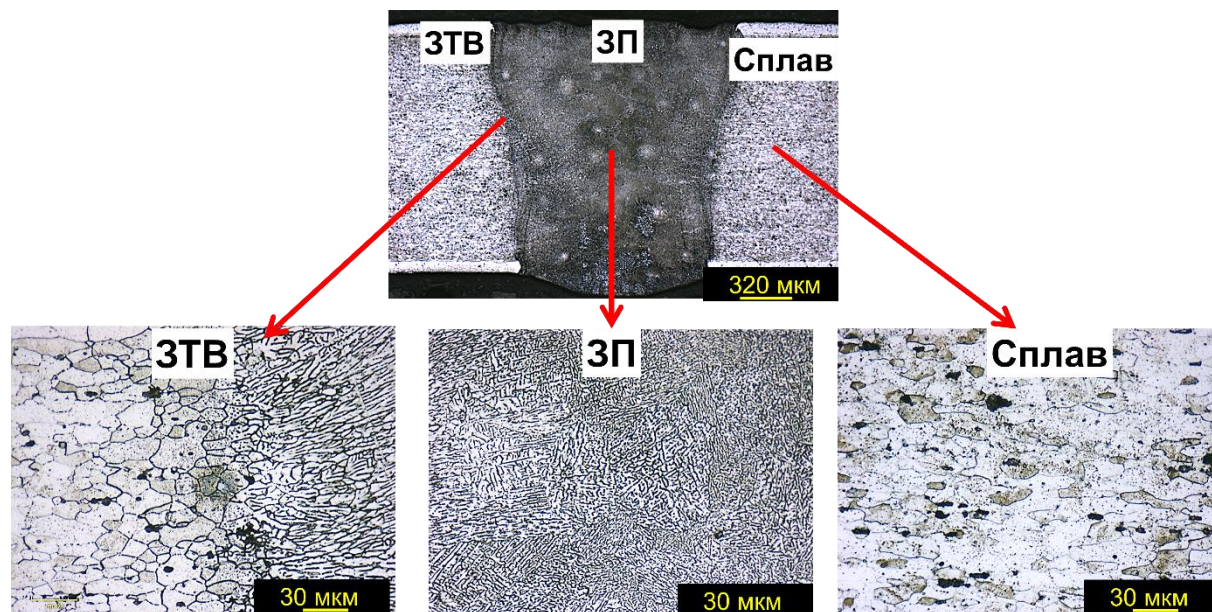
Общий вид и микроструктура поперечного сечения сварного шва и сплава Д16Т системы Al-4.4Cu-1.5Mg
